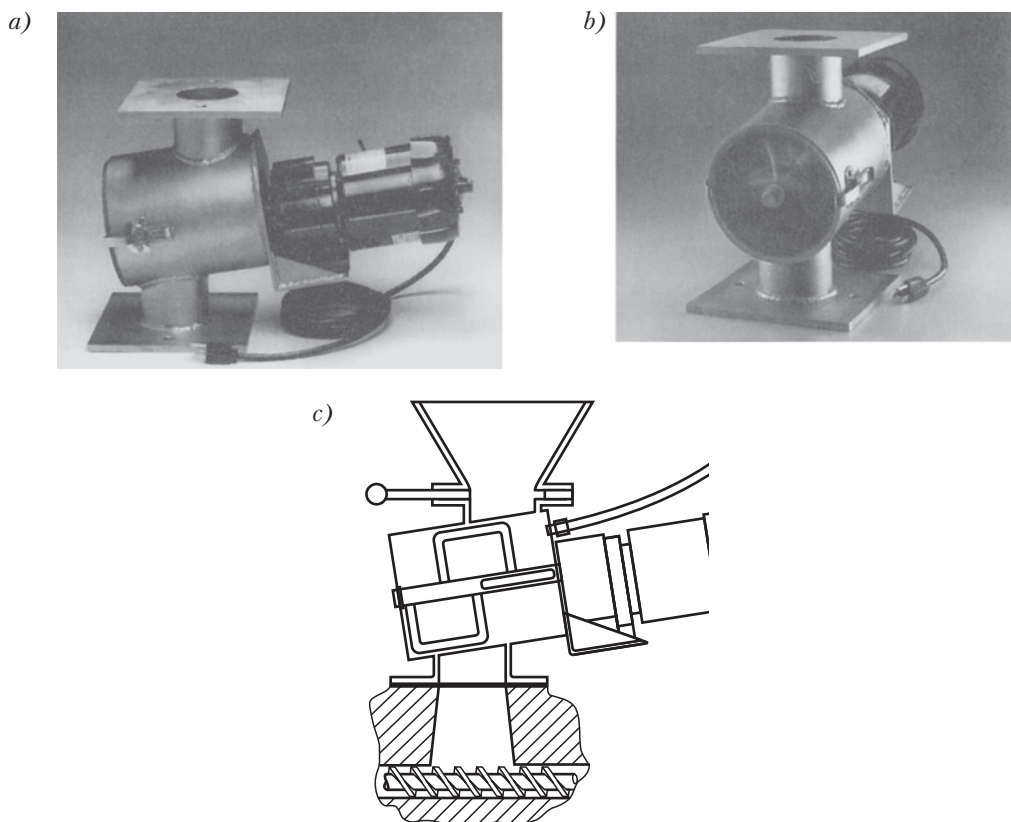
Смеситель: вид сбоку (а), фронтальный вид (b) и чертеж в разрезе (с)
